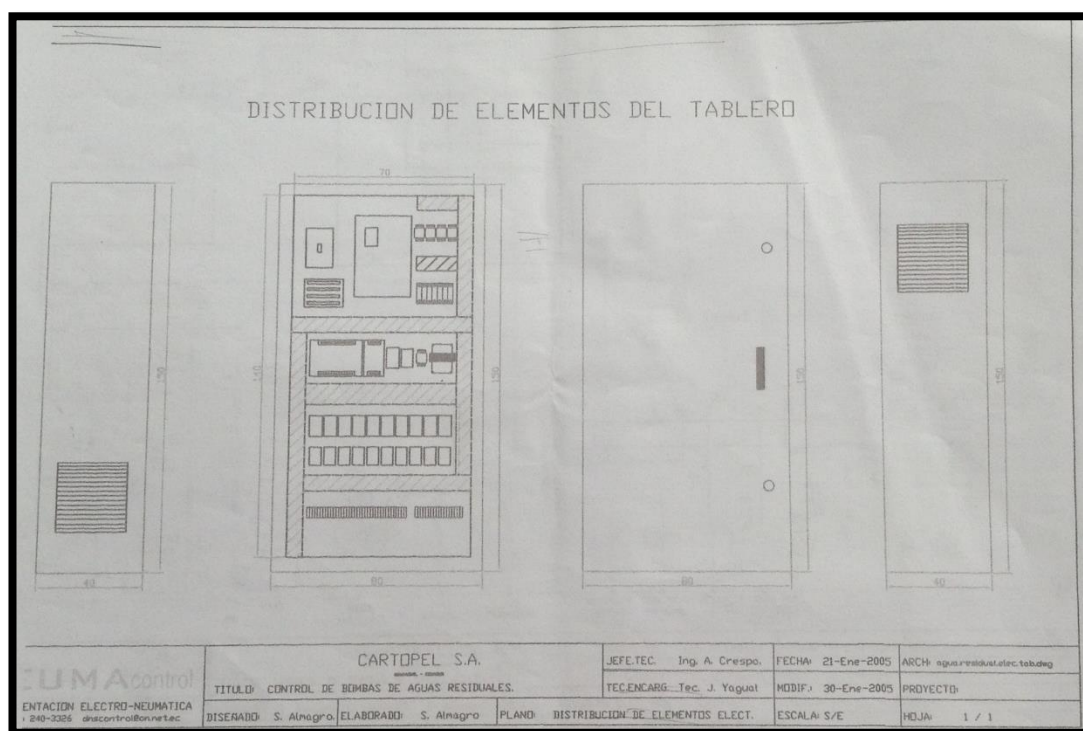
Antiguos planos de distribución del tablero. Diseño de vista interior y exterior del tablero anterior de la planta de aguas residuales.
